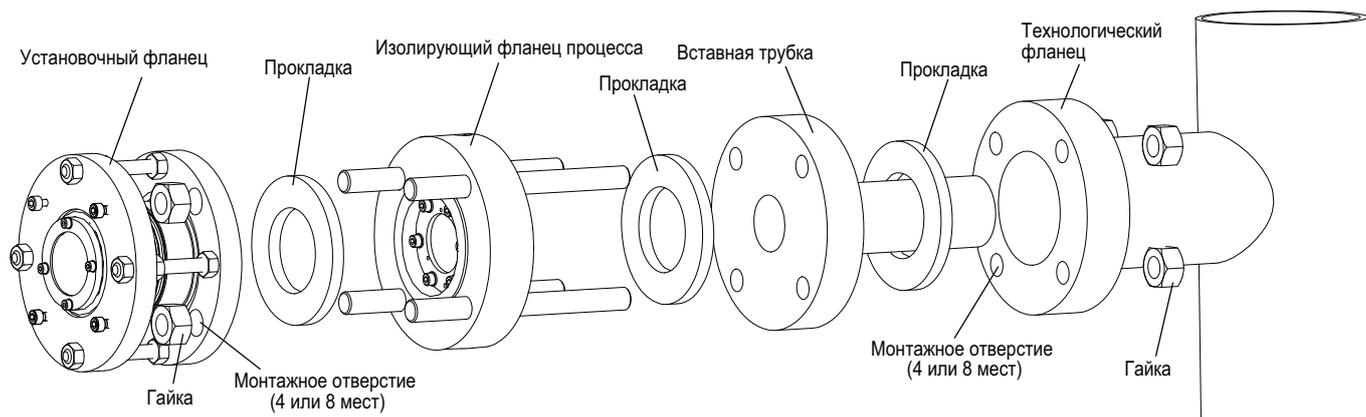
Установка вставной трубки, изолирующего фланца процесса и установочного фланца
